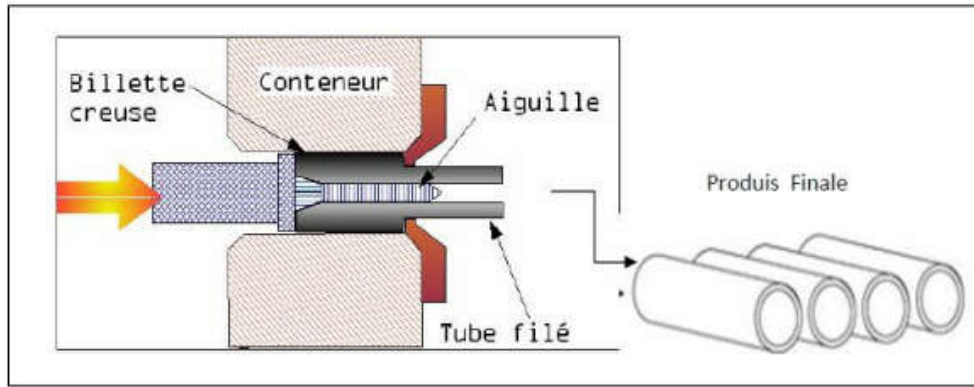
Obtention des tubes sans soudure [10]
